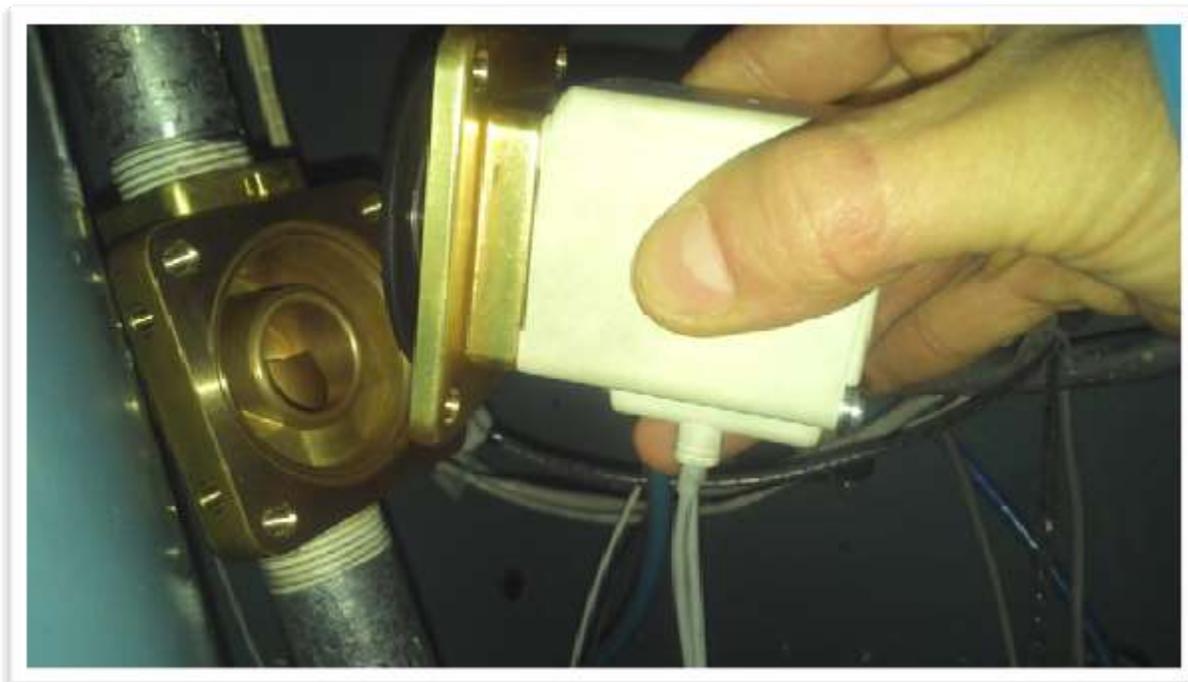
Colocación de dispositivo de válvula de diafragma para su posterior atornillado.
